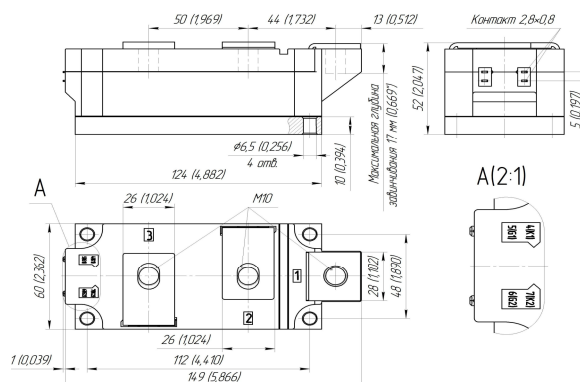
Габаритные и установочные размеры модулей типа МДЗ-580-26-А2 и МТЗ-540-18-72-А1
